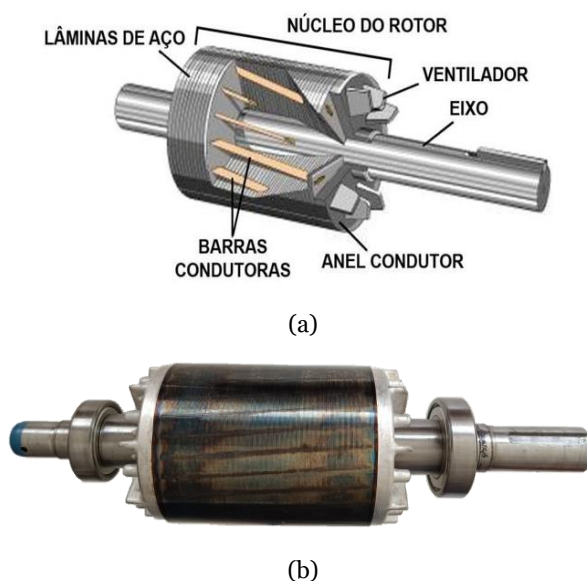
Rotor em gaiola de esquilo: (a) Partes constituintes do rotor [17]; (b) Rotor real.
